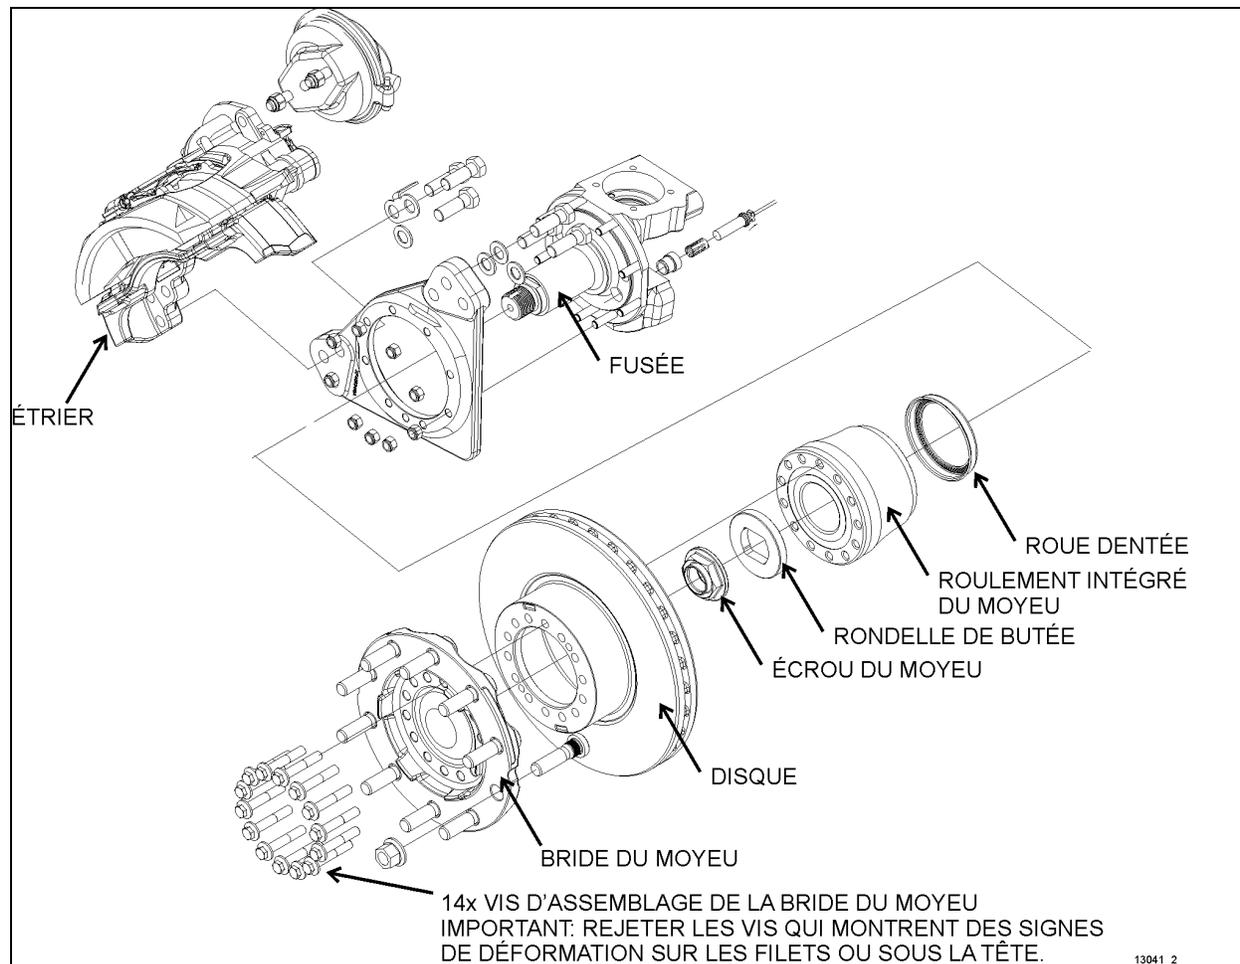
ENSEMBLE MOYEU ET DISQUE D'ESSIEU AVANT
